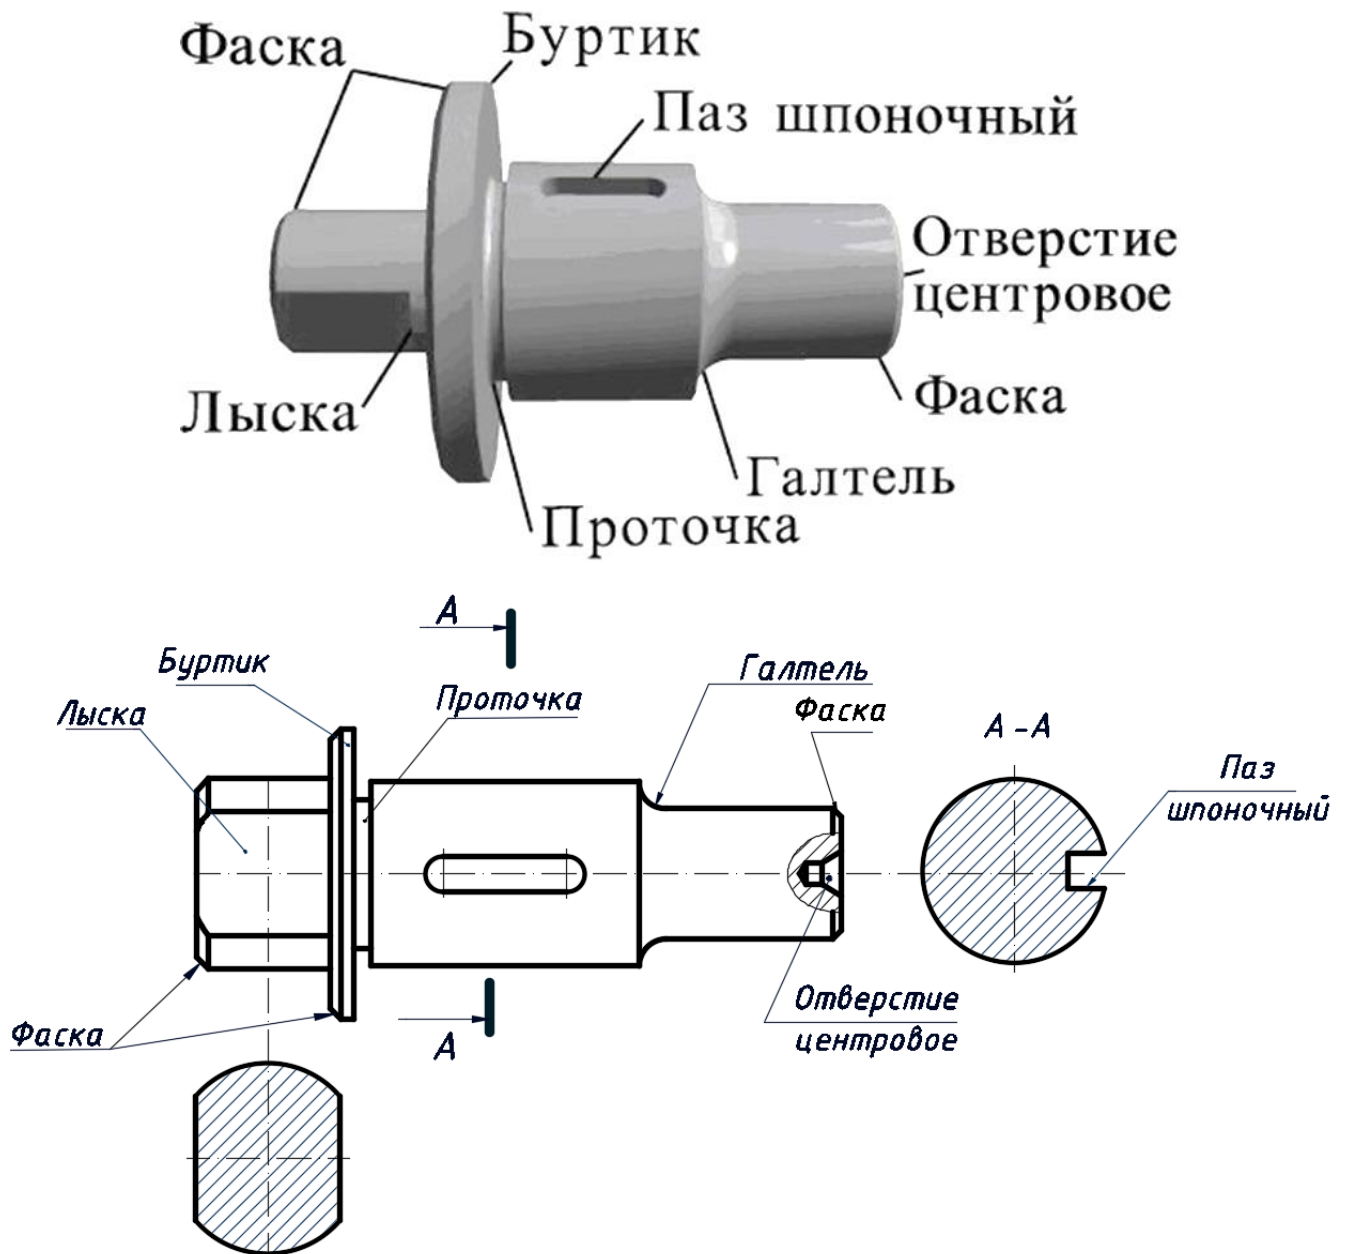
Образец выполнения конструктивных элементов детали типа «Вал».
